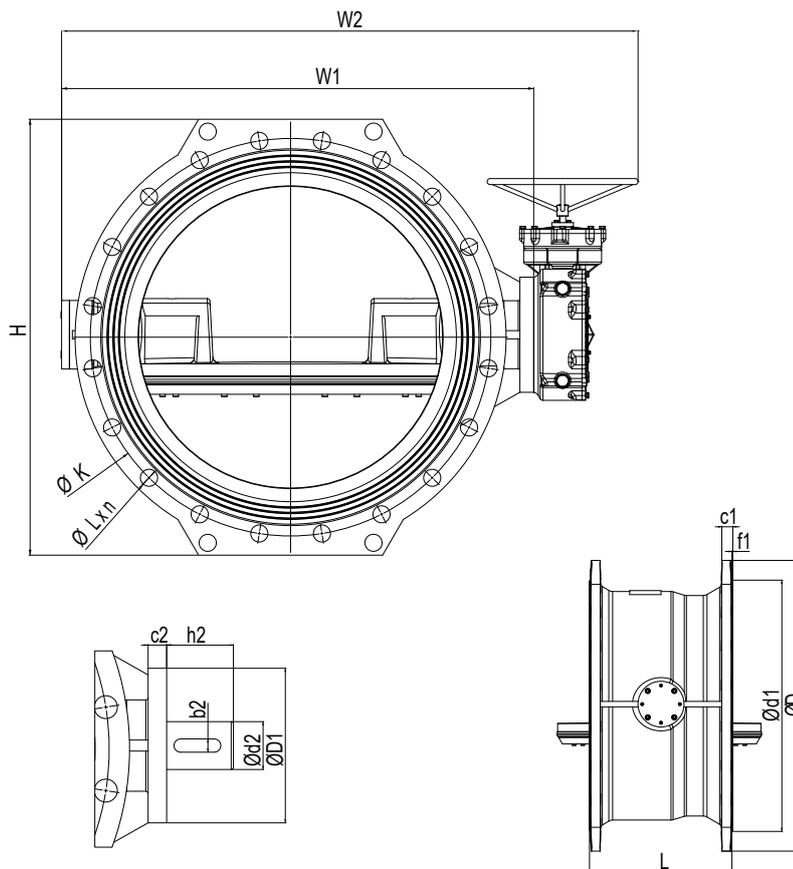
Disegno di sezione PN 25 DN 700 - 1000
